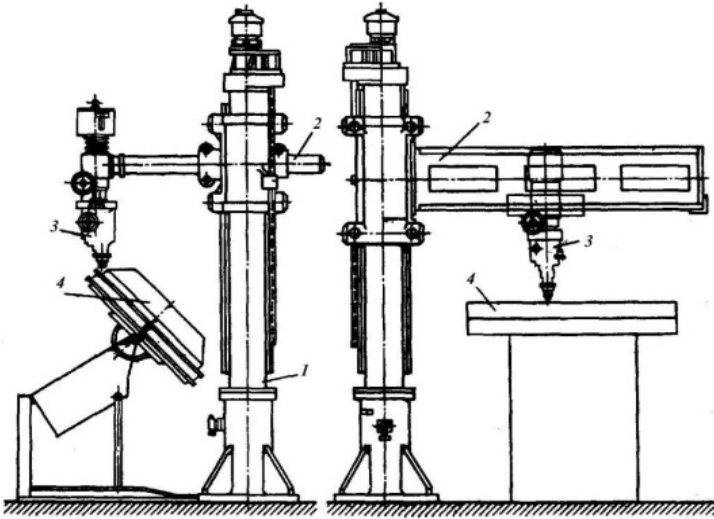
Консоль колонны для сварочных автоматов
